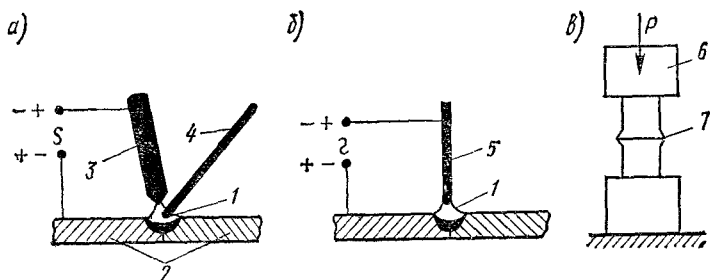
Сварка по методу Бенардоса (а); по методу Славянова (б); сварка деталей пластическим деформированием (в)
